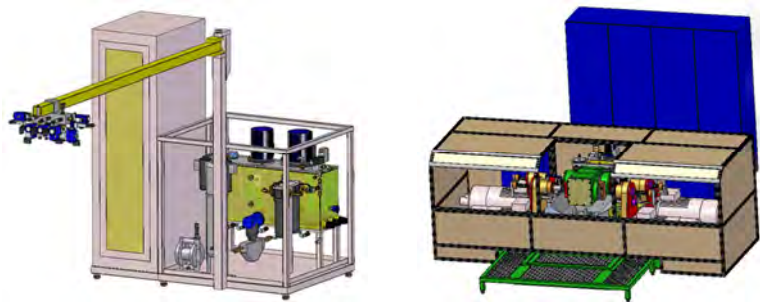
D BANCOS DE FUGA Y RODADURA
